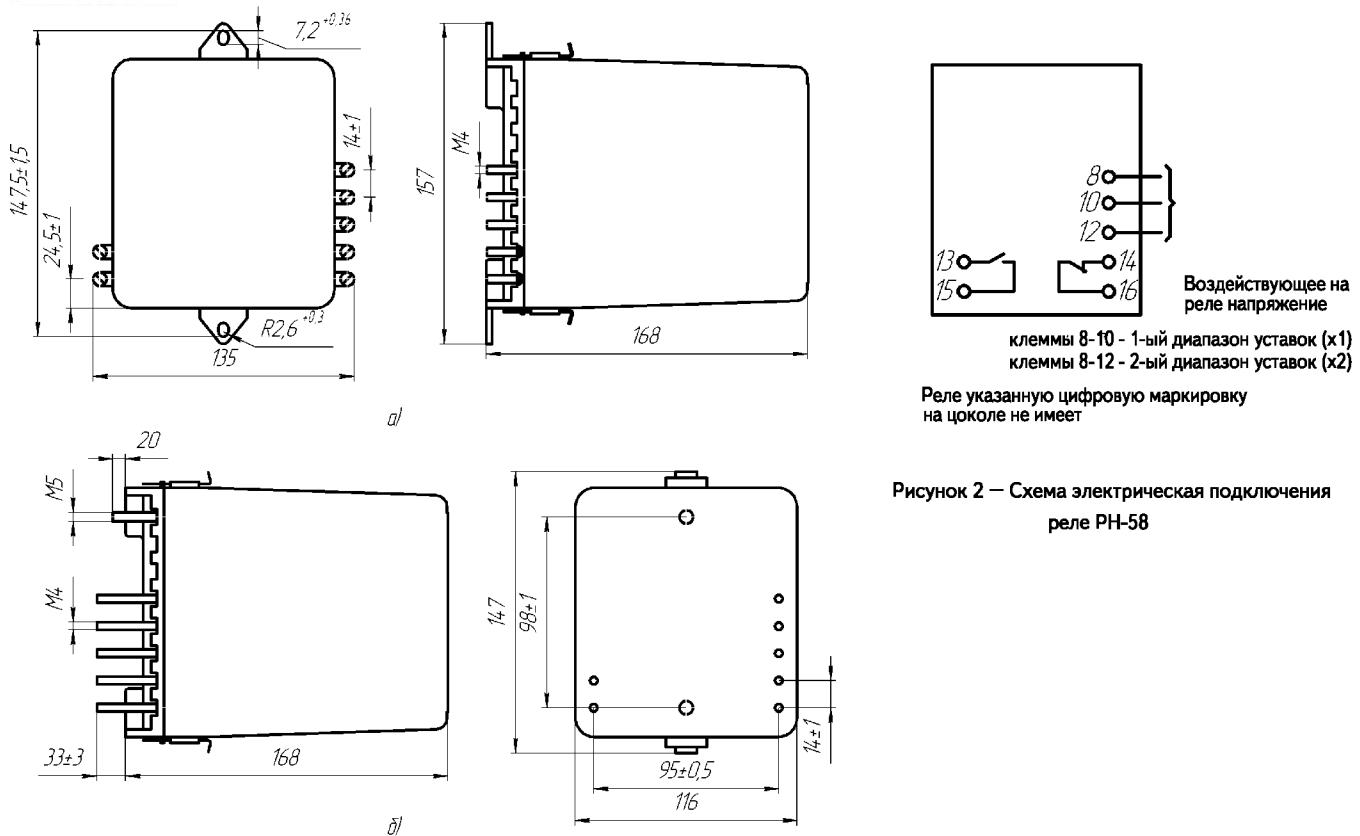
Габаритные, установочные и присоединительные размеры реле типа РН-58
